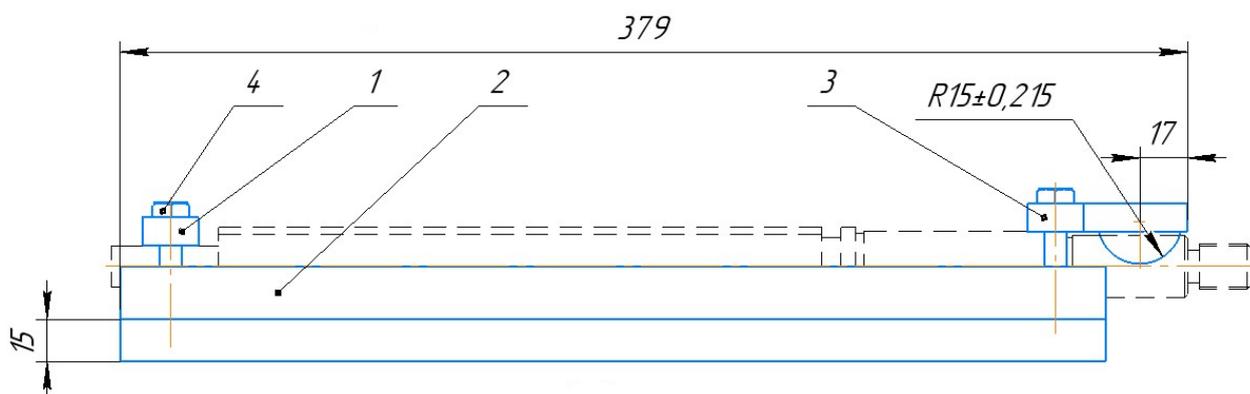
Схема приспособления для фрезерной чистовой операции
